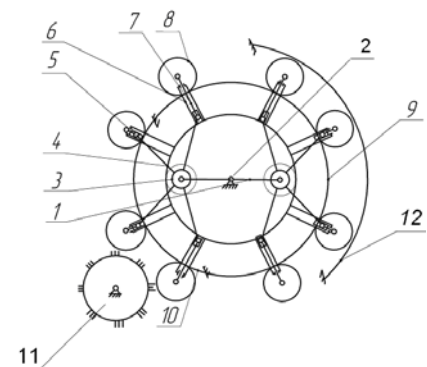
Хлопкоуборочный аппарат с планетарным механизмом привода шпинделей
